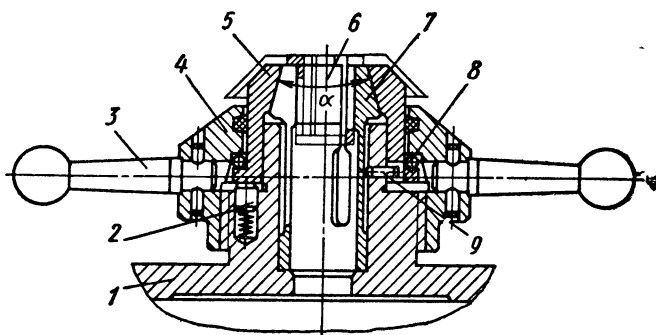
Цанговый механизм, центрирующий деталь по наружной поверхности
